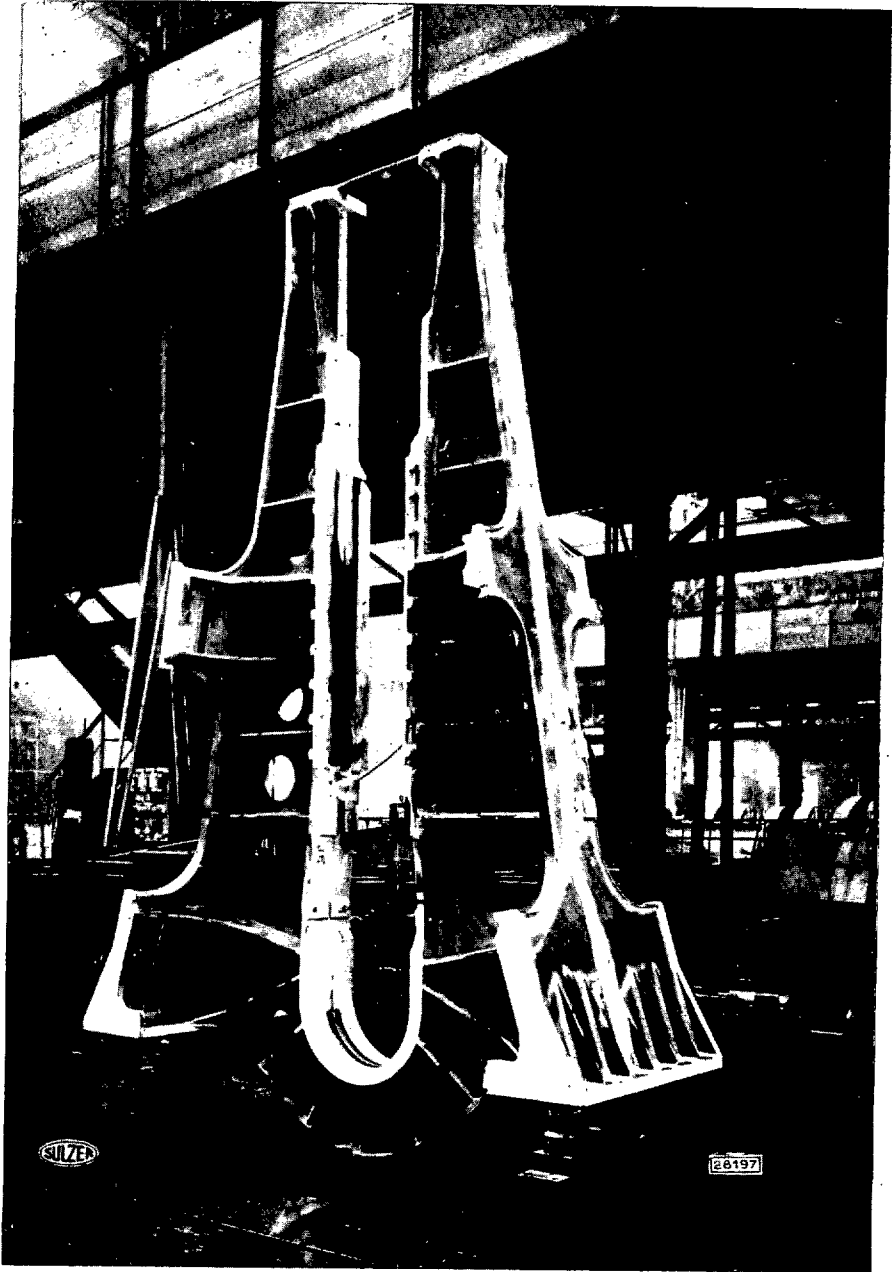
Montante soldado en plancha de acero. (Patente Sulzer)
